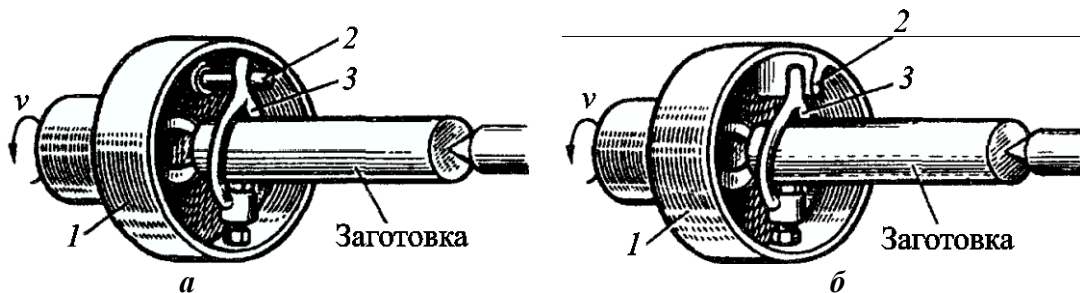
Передача обертання на заготовку за допомогою хомутика:
